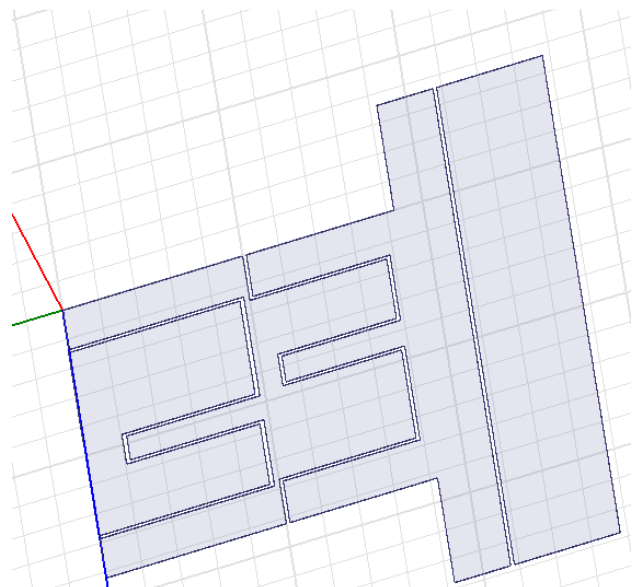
Diseño de placas del Lay-out 3 del 5L-ANPC industrial.
